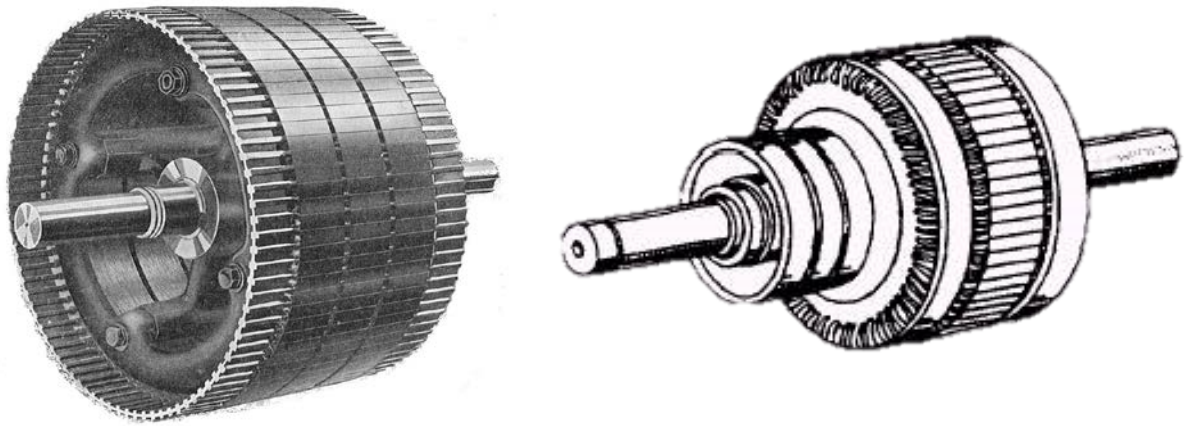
Rotor em gaiola de esquilo e rotor bobinado [5]
